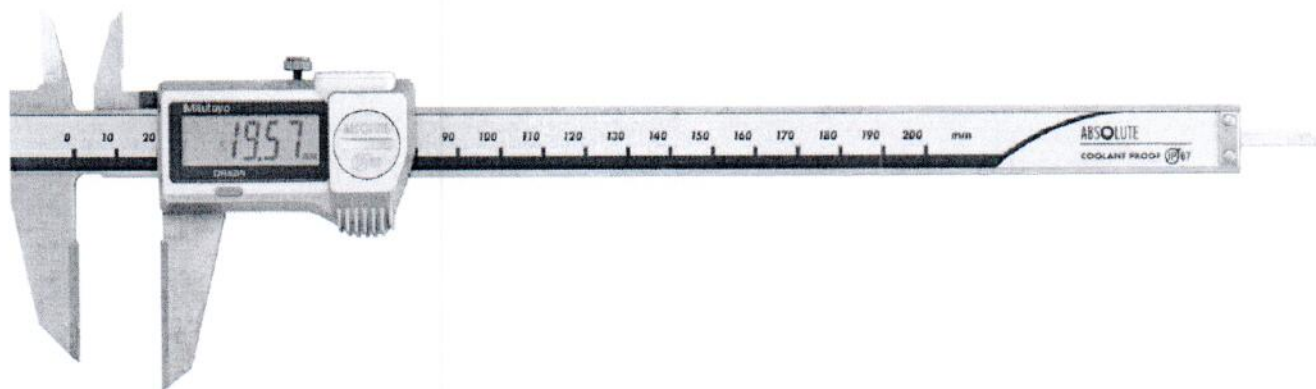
Внешний вид штангенциркуля Absolute Digimatic серии 573 с твердосплавными губками
